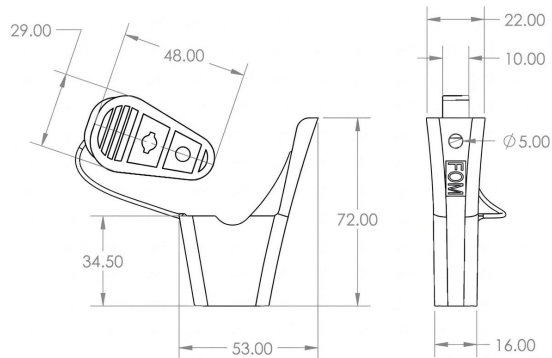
Dimensiones del cuerpo del tensor HGS-PA-120-NY
